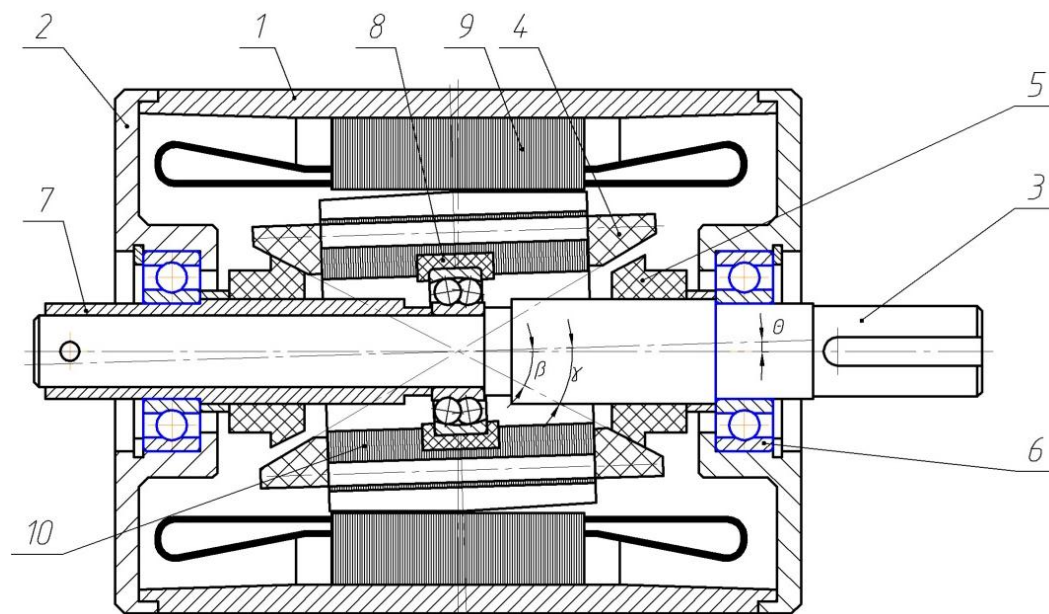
Общий вид конструкции прецессионного магнитного редуктора с фрикционным зацеплением
